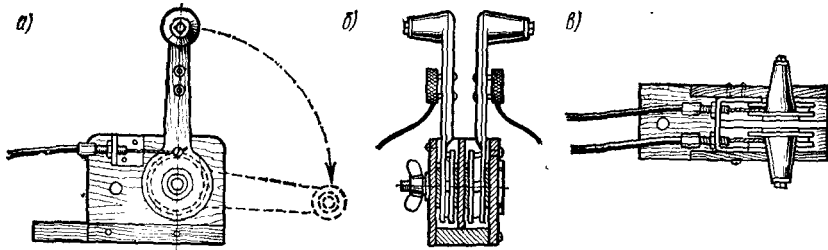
Рукоятки газа двух двигателей: а — вид сбоку; б — вид спереди; в — вид сверху.
